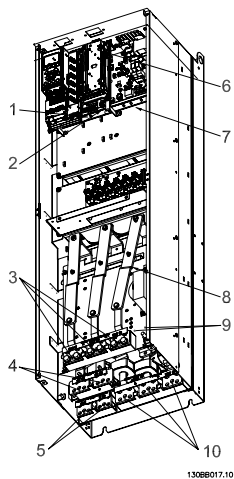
Compact IP 00 (Шасси), размер корпуса D3
